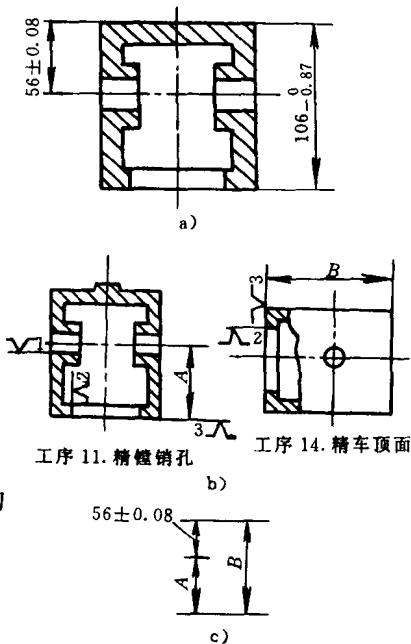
基准不重合时工序尺寸与公差确定
